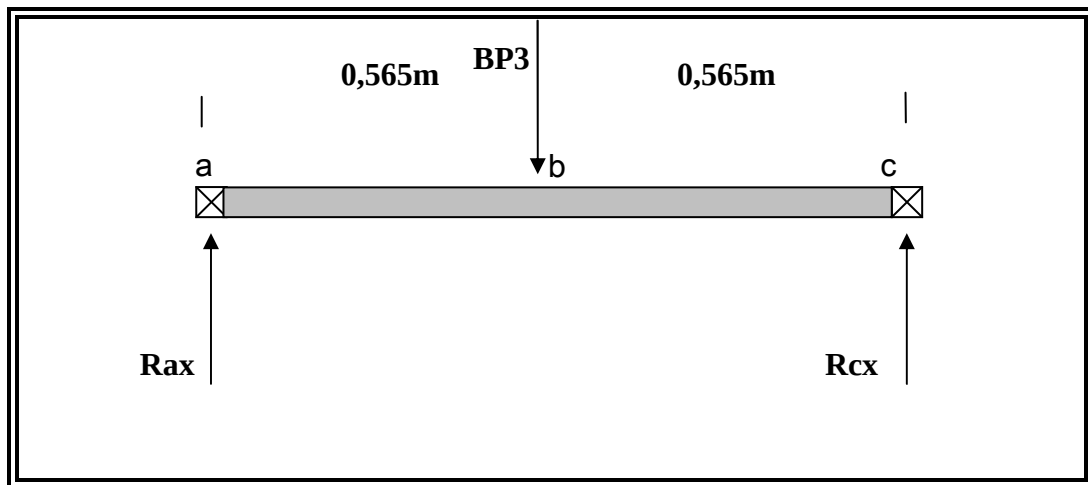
Fuerzas aplicadas sobre el eje en el plano “XZ” transportador N° 3. Fuente:
